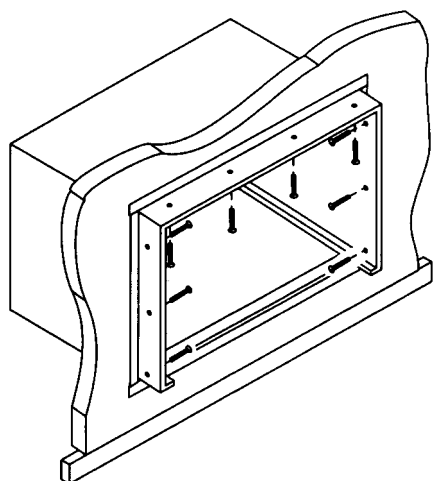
FIXATION DU CAISSON AU CADRE
